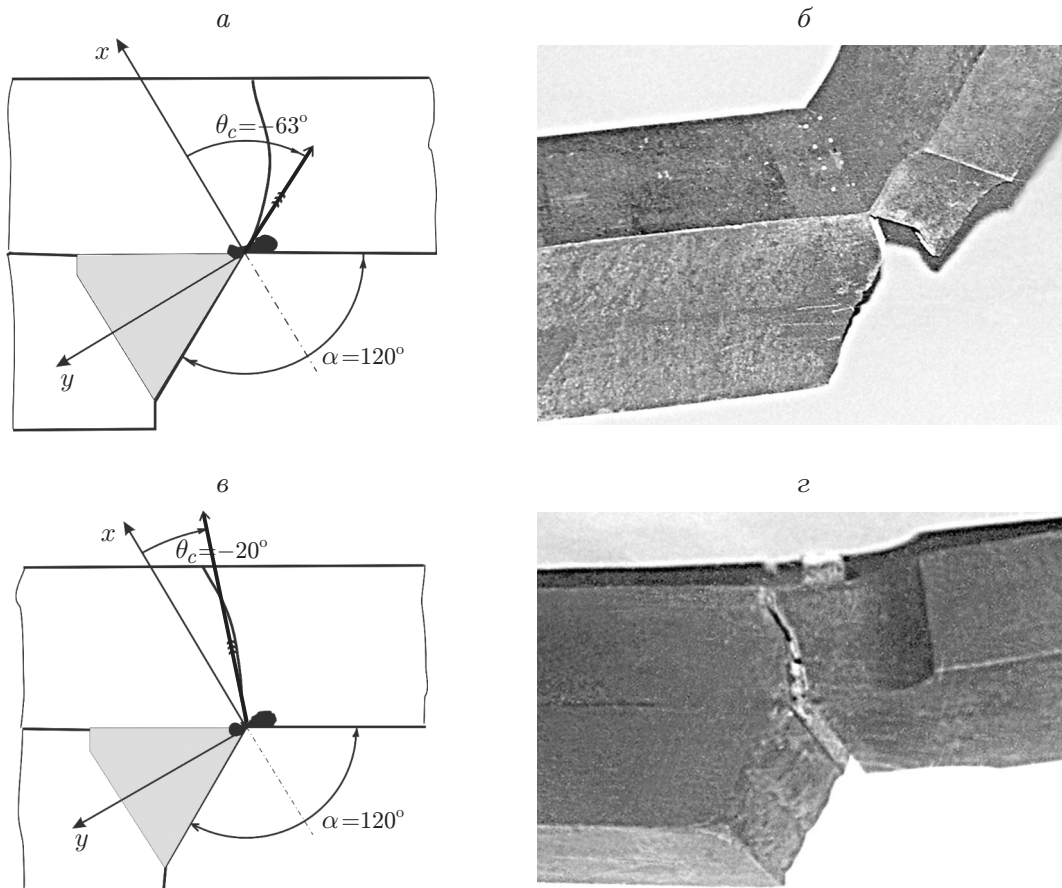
Схемы разрушения (а, в) и фотографии разрушенного сварного образца (б, г):
